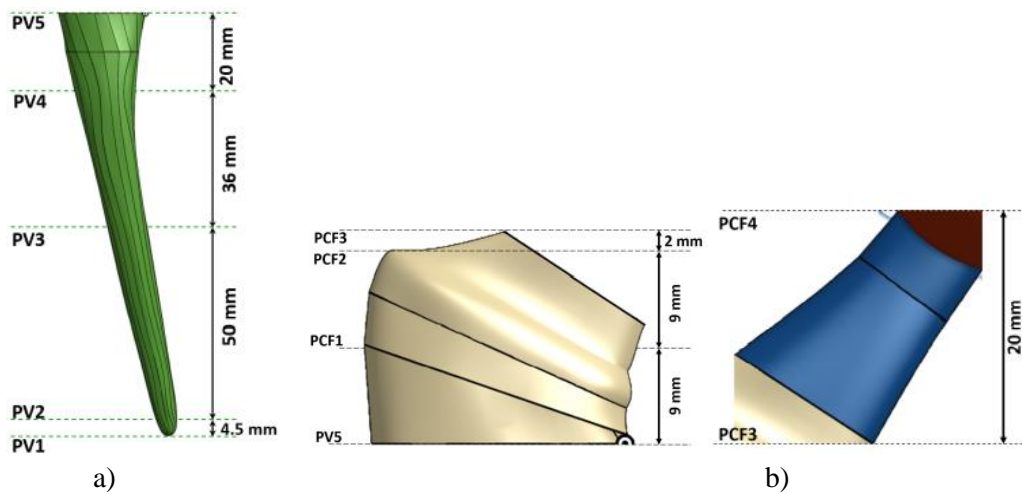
Dimensiones de la prótesis, a) Dimensiones vástago y b) Dimensiones cuello femoral (Hernández, 2020)
